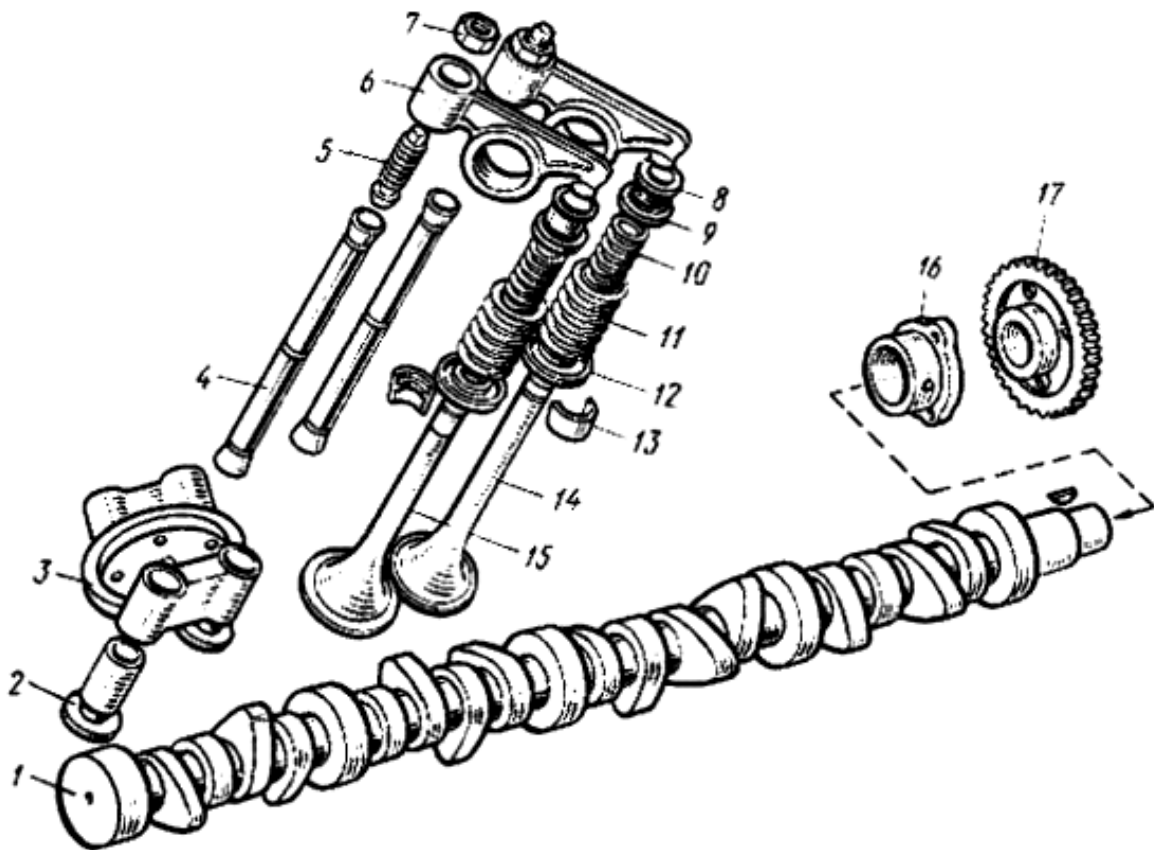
Схема Газорозподільного механізму: 1 - розподільний вал; 2 - штовхач; 3 - напрямний штовхач; 4 - штанга; 5- гвинт регулювання; 6 - коромисло; 7 - контргайка; 8 - втулка; 9 - тарілка; 10 - внутрішня пружина; 11 - зовнішня пружина; 12 - шайба; 13 - сухар; 14 - впускний клапан; 15 - випускний клапан; 16 - фланець; 17 - шестерня;
